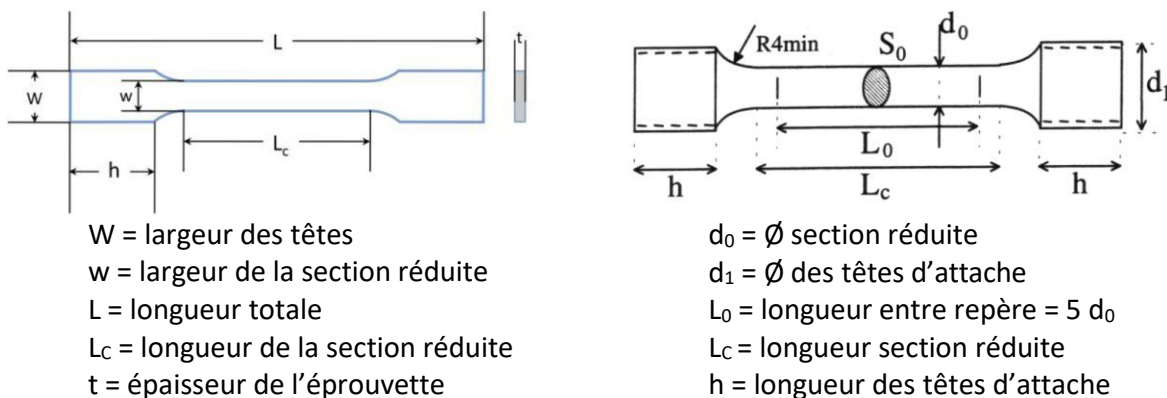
Deux exemples d'éprouvette de traction : éprouvette plate (à gauche) et éprouvette cylindrique (à droite).
